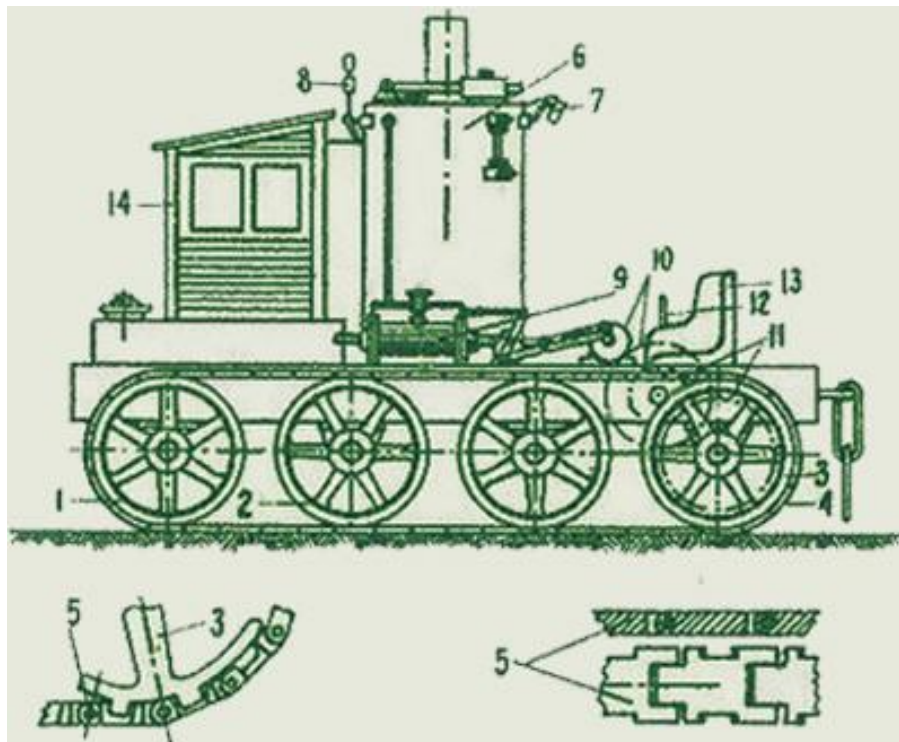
Подлинный чертеж парового трактора Фёдора Блинова, приложенный к его патентной заявке: 1 — направляющее колесо; 2 — опорные катки; 3— ведущее колесо; 4— гусеница; 5 — звенья гусеницы; 6— паровой котел; 7 — манометр; 8 — свисток; 9 — паровая машина; 10 — первая пара шестерен; 11 — вторая пара шестерен; 12 — рычаг управления; 13 — сиденье машиниста; 14 — будка управления.
